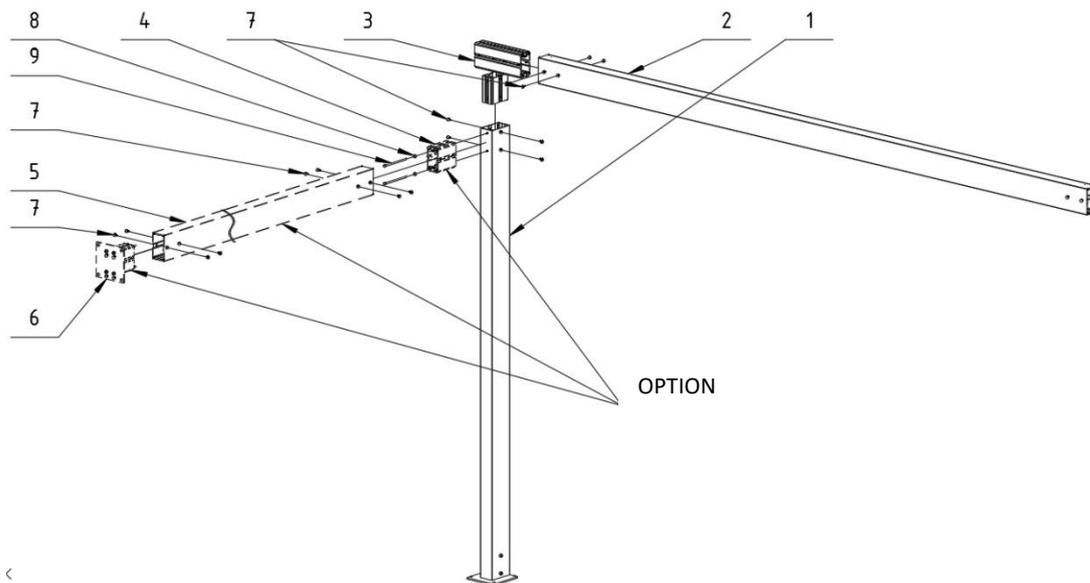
Méthode d'installation du module suivant (intermédiaire/fermeture) : 1 – Poteau bas, 2 - Poutre avant (gauche / droite) ou Poutre avant (intermédiaire), 3 Connecteur "Connexion module", 4 - Connecteur linéaire (option), 5 Poutre latérale (option), 6 - Pied arrière (option), 7 - Vis M8x16, 8 Rondelle  $\varnothing 8.4$  (option), 9 - Vis M8x180 (option).
